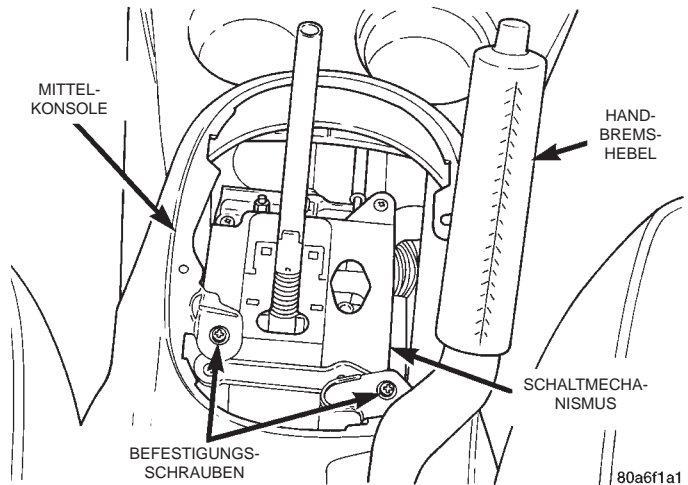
Vordere Befestigungsschraube der Mittelkonsole
